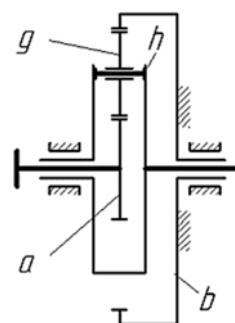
Планетарный редуктор с одновенцовым сателлитом
